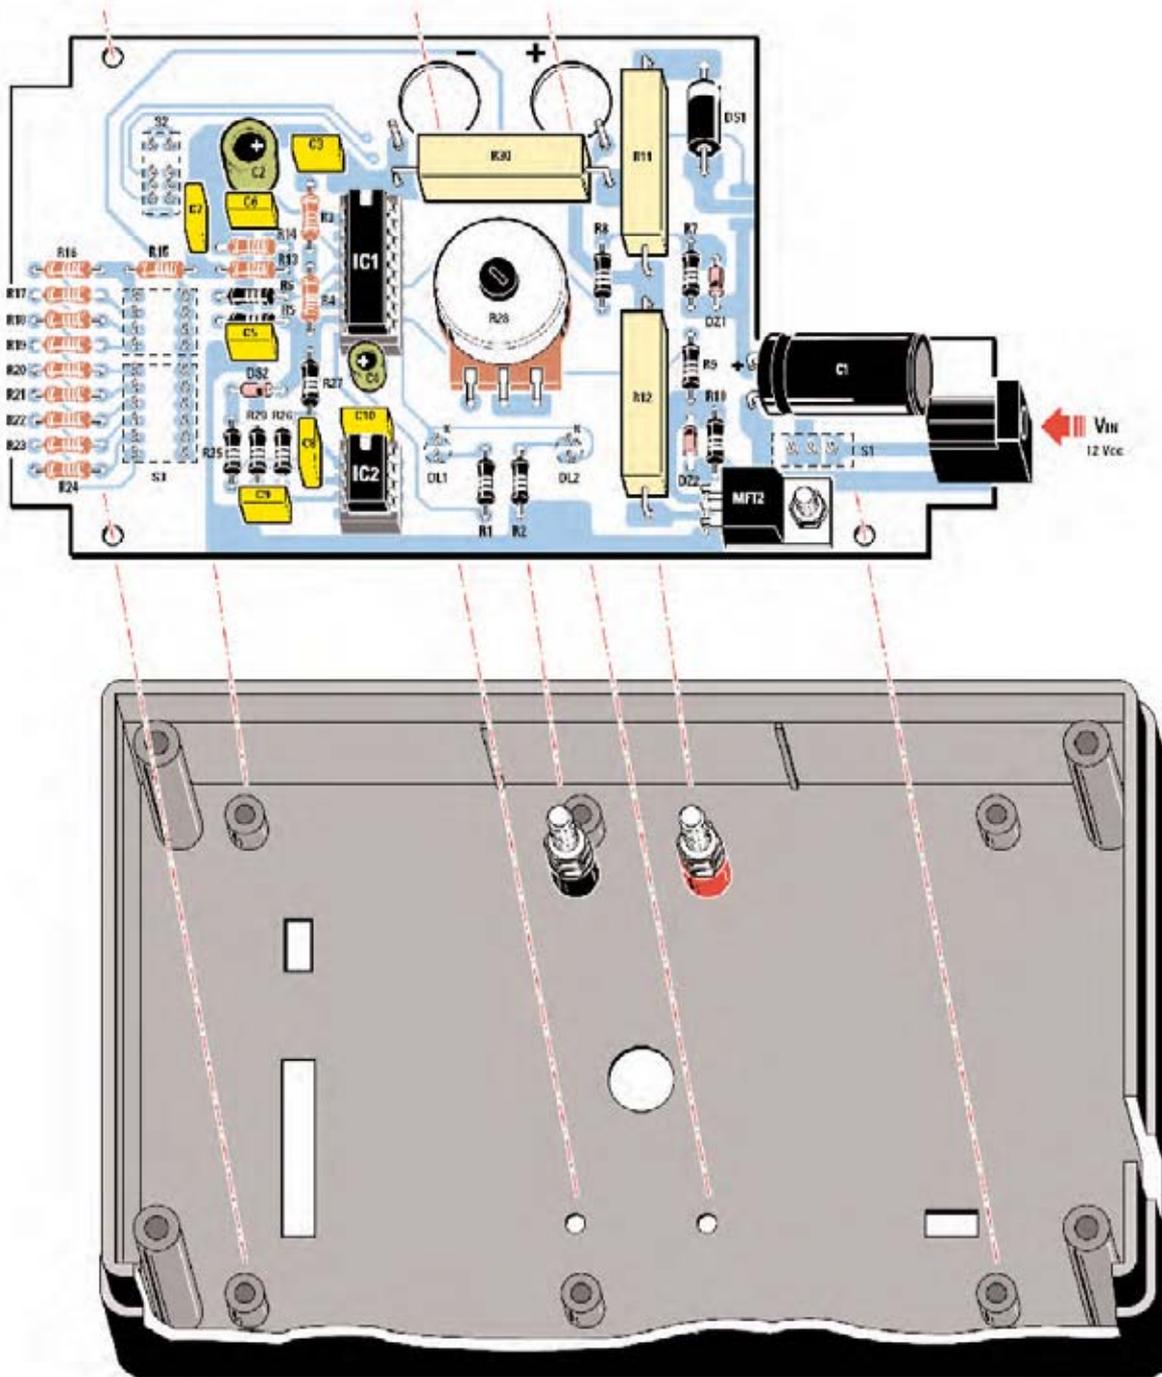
El circuito impreso, con todos sus componentes montados, ha de instalarse en la parte interna del panel frontal del mueble en la posición aquí indicada.
